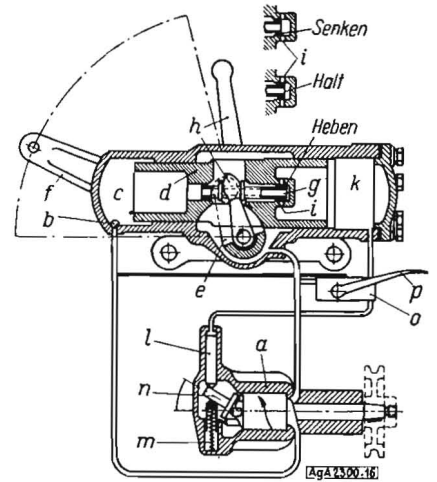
Pentax-Kraftheber von Stockey & Schmitz
